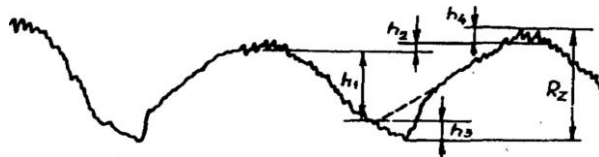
Исходная схема для расчета высоты профиля шероховатости поверхности при механической обработке
